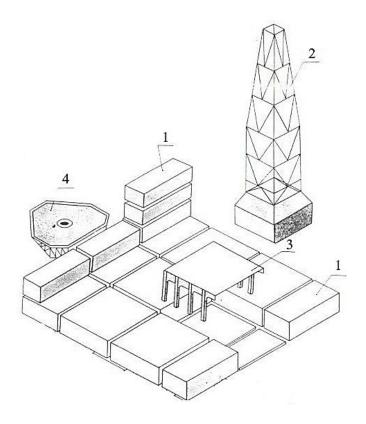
Разбивка конструкций ППБУ на сборочно-монтажные единицы (верхняя часть):
